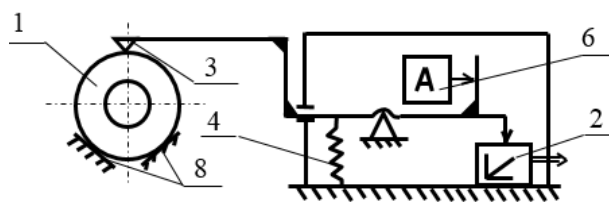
Вимірювальний пристрій для контролю зовнішнього діаметра з фіксованим базуванням деталі
